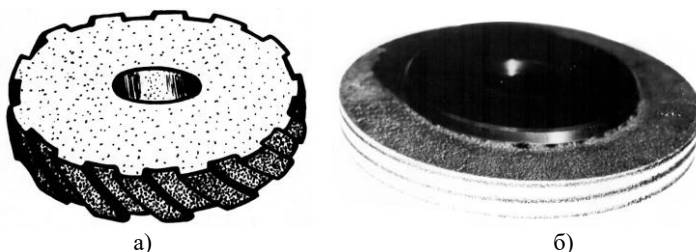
Абразивные шлифовальные круги, обеспечивающие непрерывный контакт с обрабатываемой деталью: прерывистый круг с наклонными пазами (а) и круг со спиральными канавками на рабочей поверхности (б)
